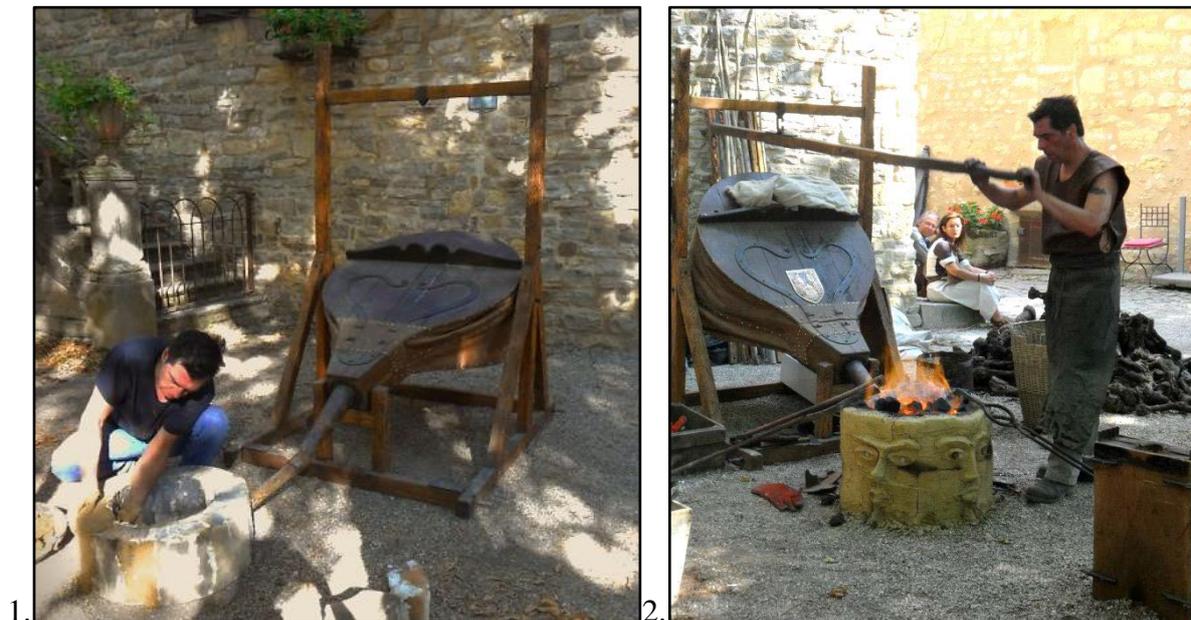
1. Mise en place d'une structure de chauffe moderne en plein air par Gilles Blazy.
